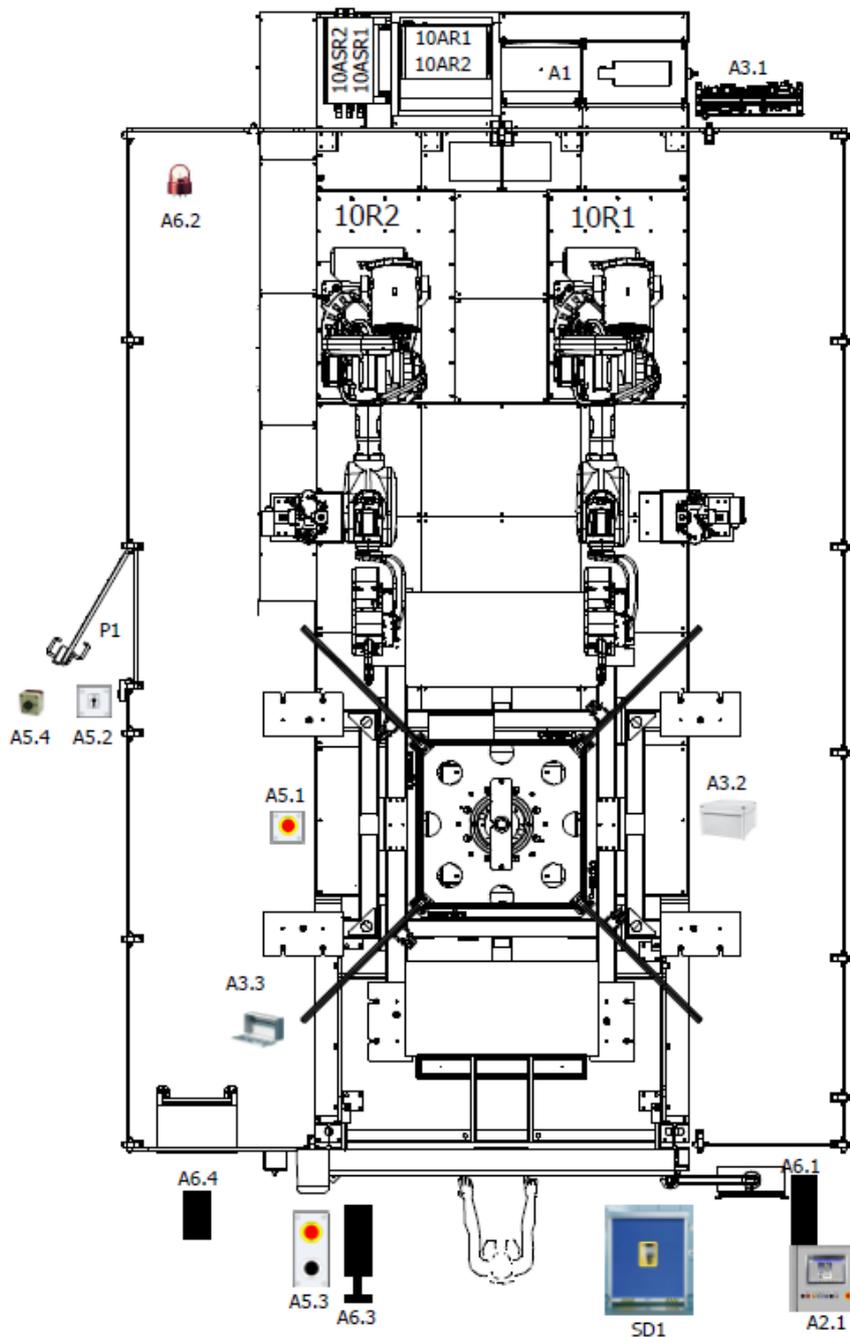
Imagen croquis en planta de la flexicélula.
